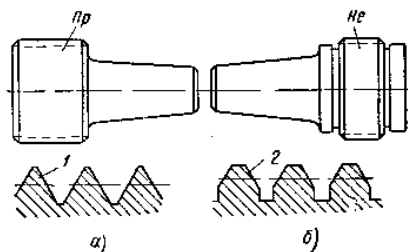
Резьбовые калибры-пробки: 1 — профиль резьбы проходного калибра, 2 — профиль непроходного калибра
